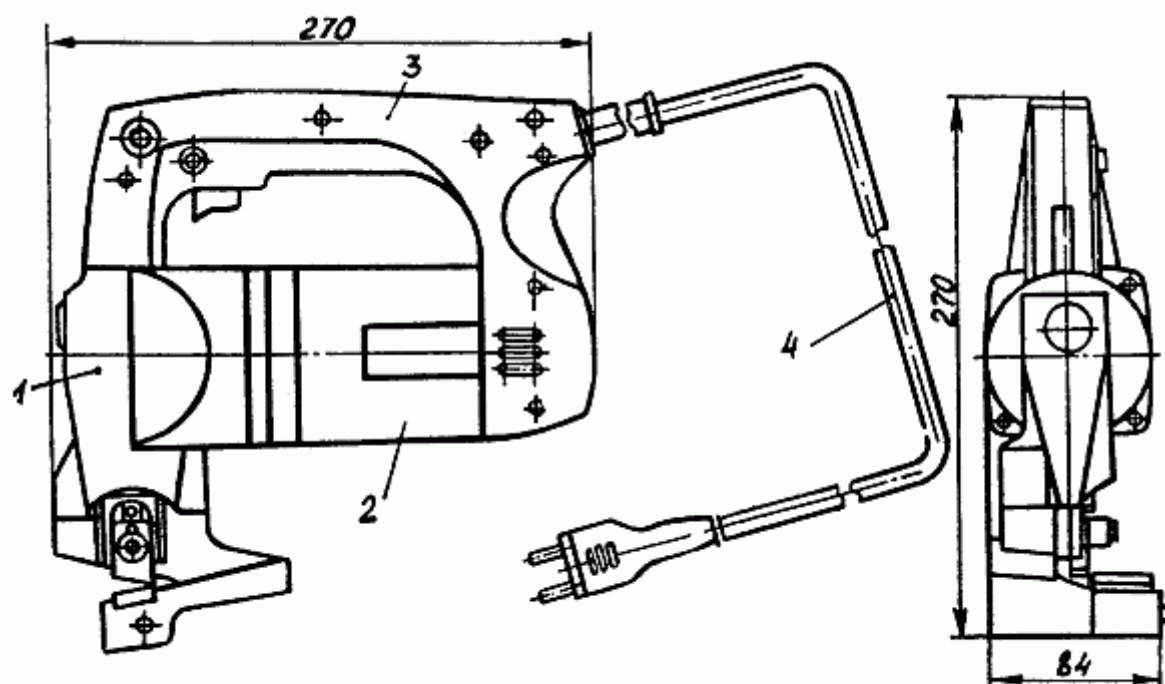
Общий вид ножниц; 1 — редуктор; 2 — электропривод; 3 — ручка с выключателем и фильтром подавления радио- и тепломех; 4 — провод соединительный.
